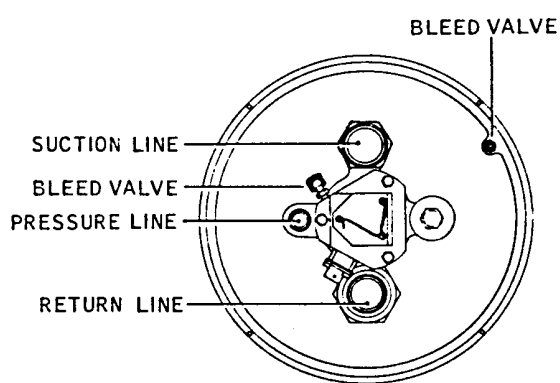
Hydraulik-Anschlüsse und Überdruckventil
